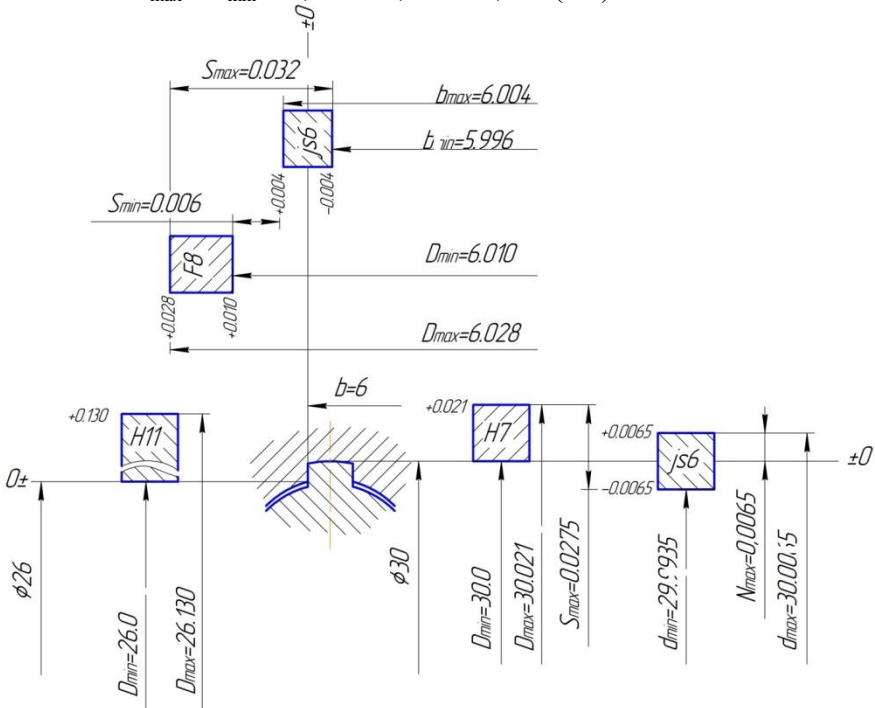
Схема розташування полів допусків шліцьового з'єднання
